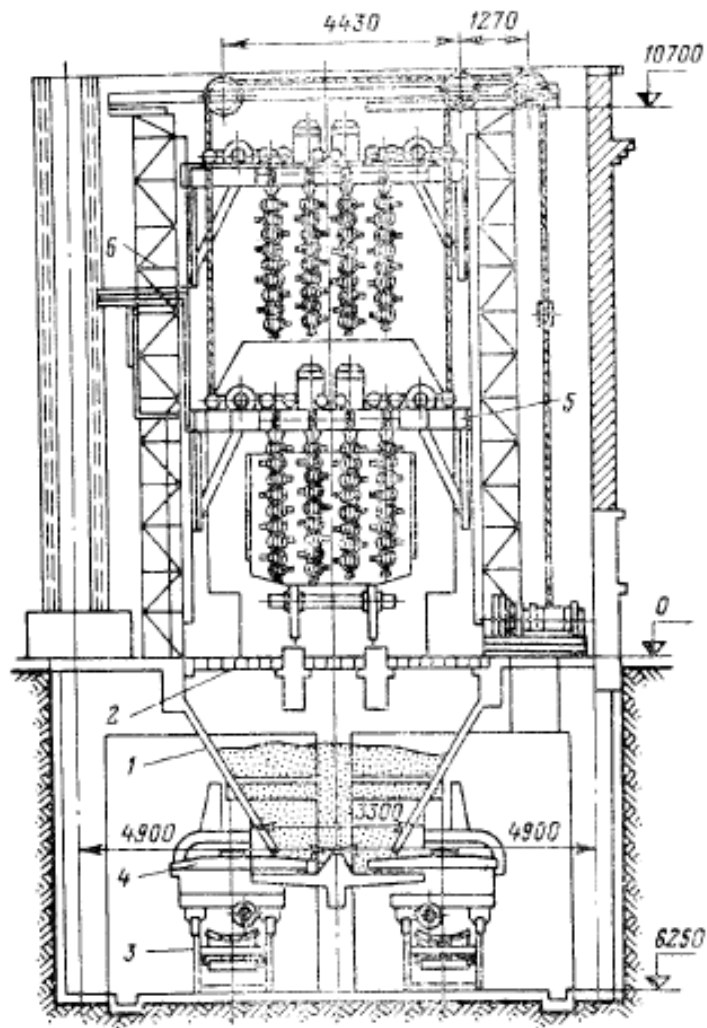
Установка бурофрезерної розпушувальної машини у бункерному прийомному пристрої:
